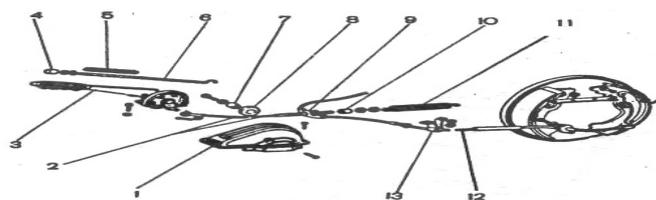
Детали привода стояночного тормоза: 1 - чехол; 2 - передний трос; 3 - рычаг; 4 - кнопка; 5 - пружина тяги; 6 - тяга защелки; 7 - втулка; 8 - ролик; 9 - направляющая заднего троса; 10 - распорная втулка; 11 - оттяжная пружина; 12 - задний трос; 13 - кронштейн заднего троса
